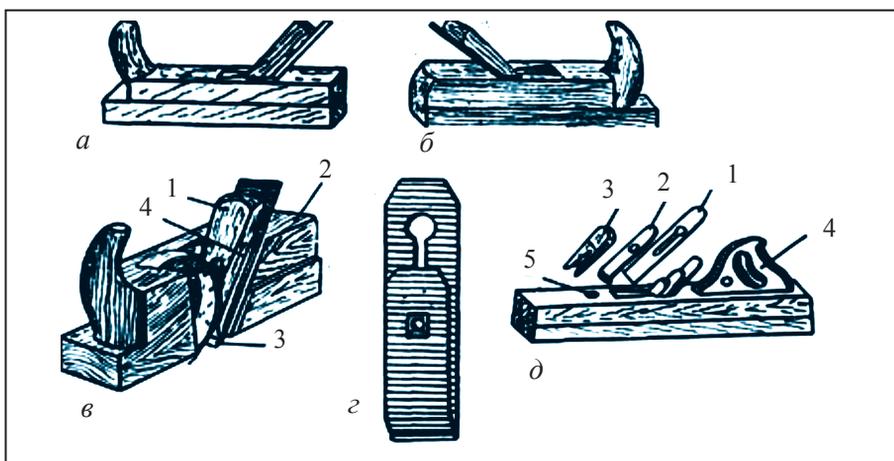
Виды рубанка: *а* – шерхебель; *б* – досочный рубанок; *в* – муштранда: 1 – клин; 2 – колода; 3 – нож; 4 – резец (железка); *г* – двойной резец; *д* – плотный рубанок (жапс ранда): 1 – нож; 2 – резец; 3 – клин; 4 – ручка; 5 – кнопка кования.
